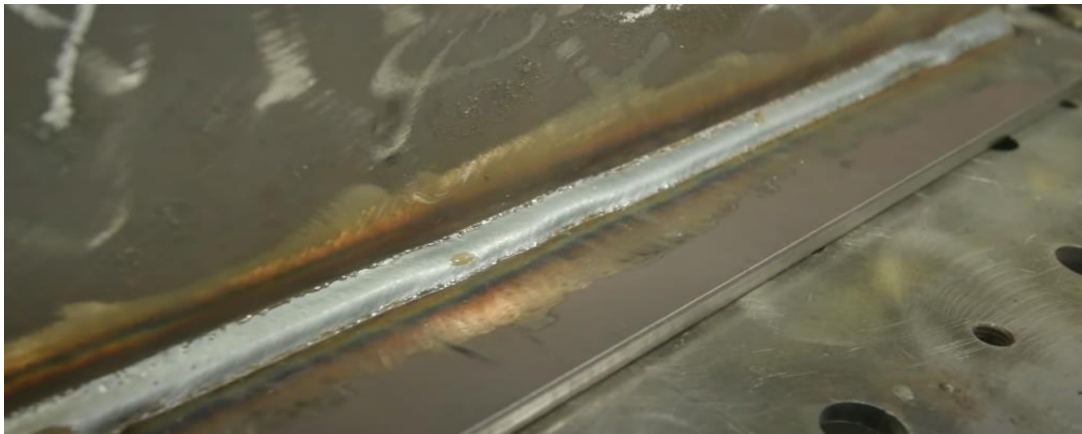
Зразок зварного шва, виконаний в режимі струменевого перенесення металу
